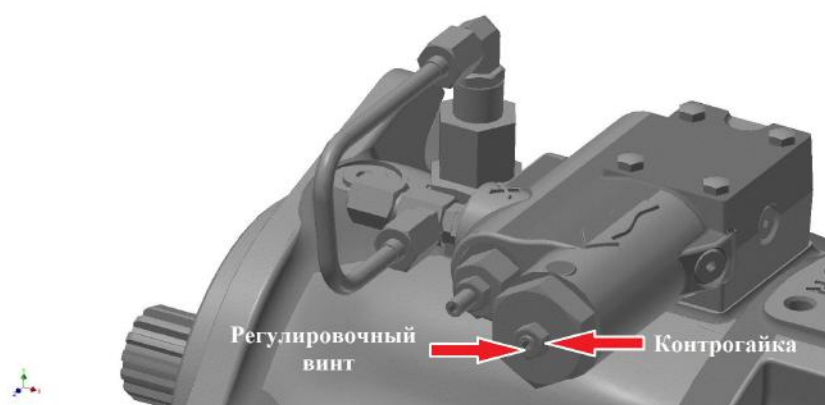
Регулировка срабатывания компенсатора давления
